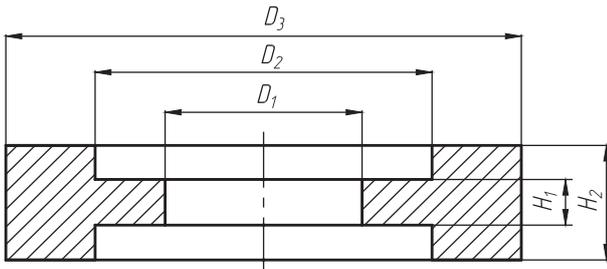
Эскиз типовой поковки «шестерня цилиндрическая ведомая» заднего моста автомобиля КаМАЗ
